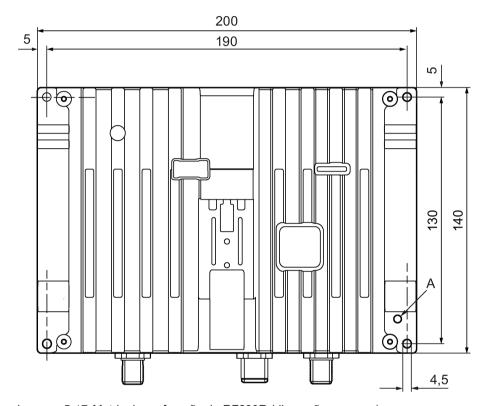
Matriz de perfuração do RF290R (dimensões em mm)
